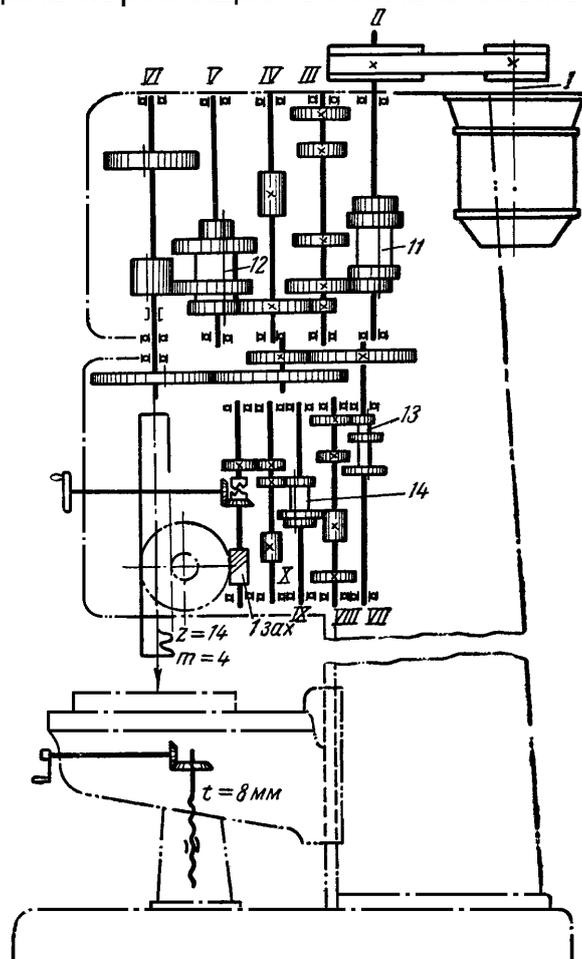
Упрощенная кинематическая схема сверлильного станка
